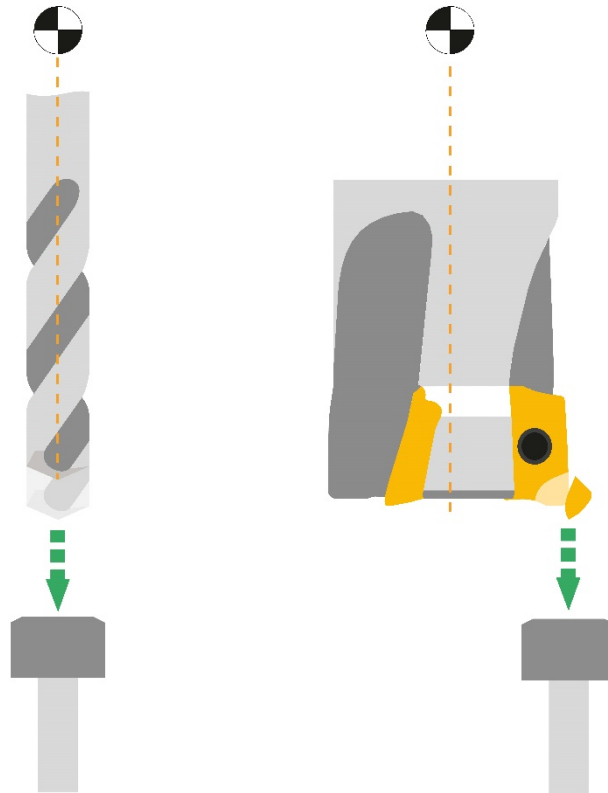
Überprüfung auf Werkzeugbruch bei rotierendem Werkzeug
